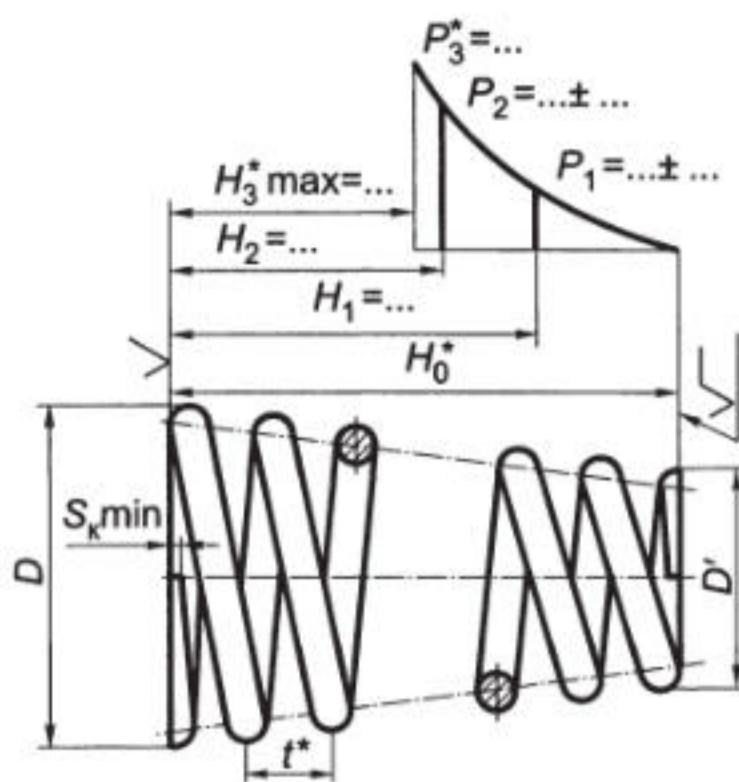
Пружина сжатия коническая из проволоки круглого сечения с поджатыми на $\frac{3}{4}$ витка концами и шлифованными на $\frac{3}{4}$ окружности опорными поверхностями
